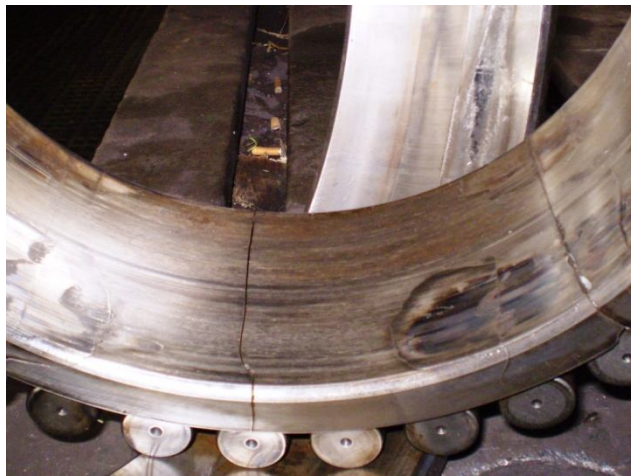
Кольцевые риски на торцевой поверхности внутреннего кольца – результат контакта кольца подшипника с неподвижной деталью
